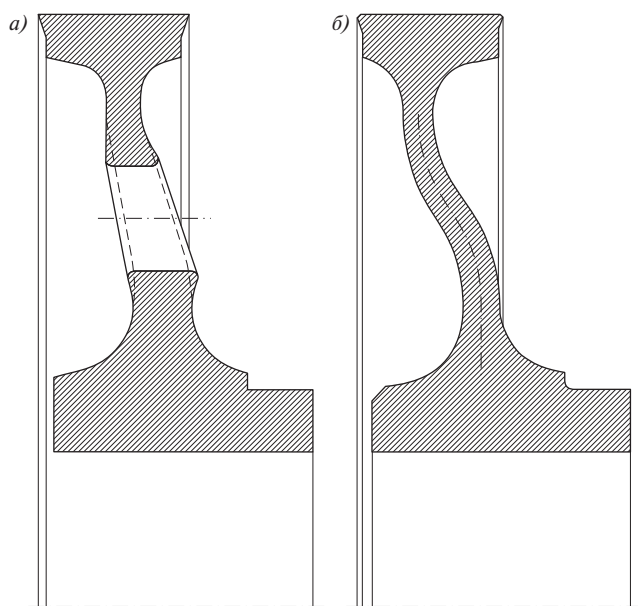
Конструкция центра колесного для тепловозов 2ТЭ10, 2ТЭ116, ТЭМ2:
